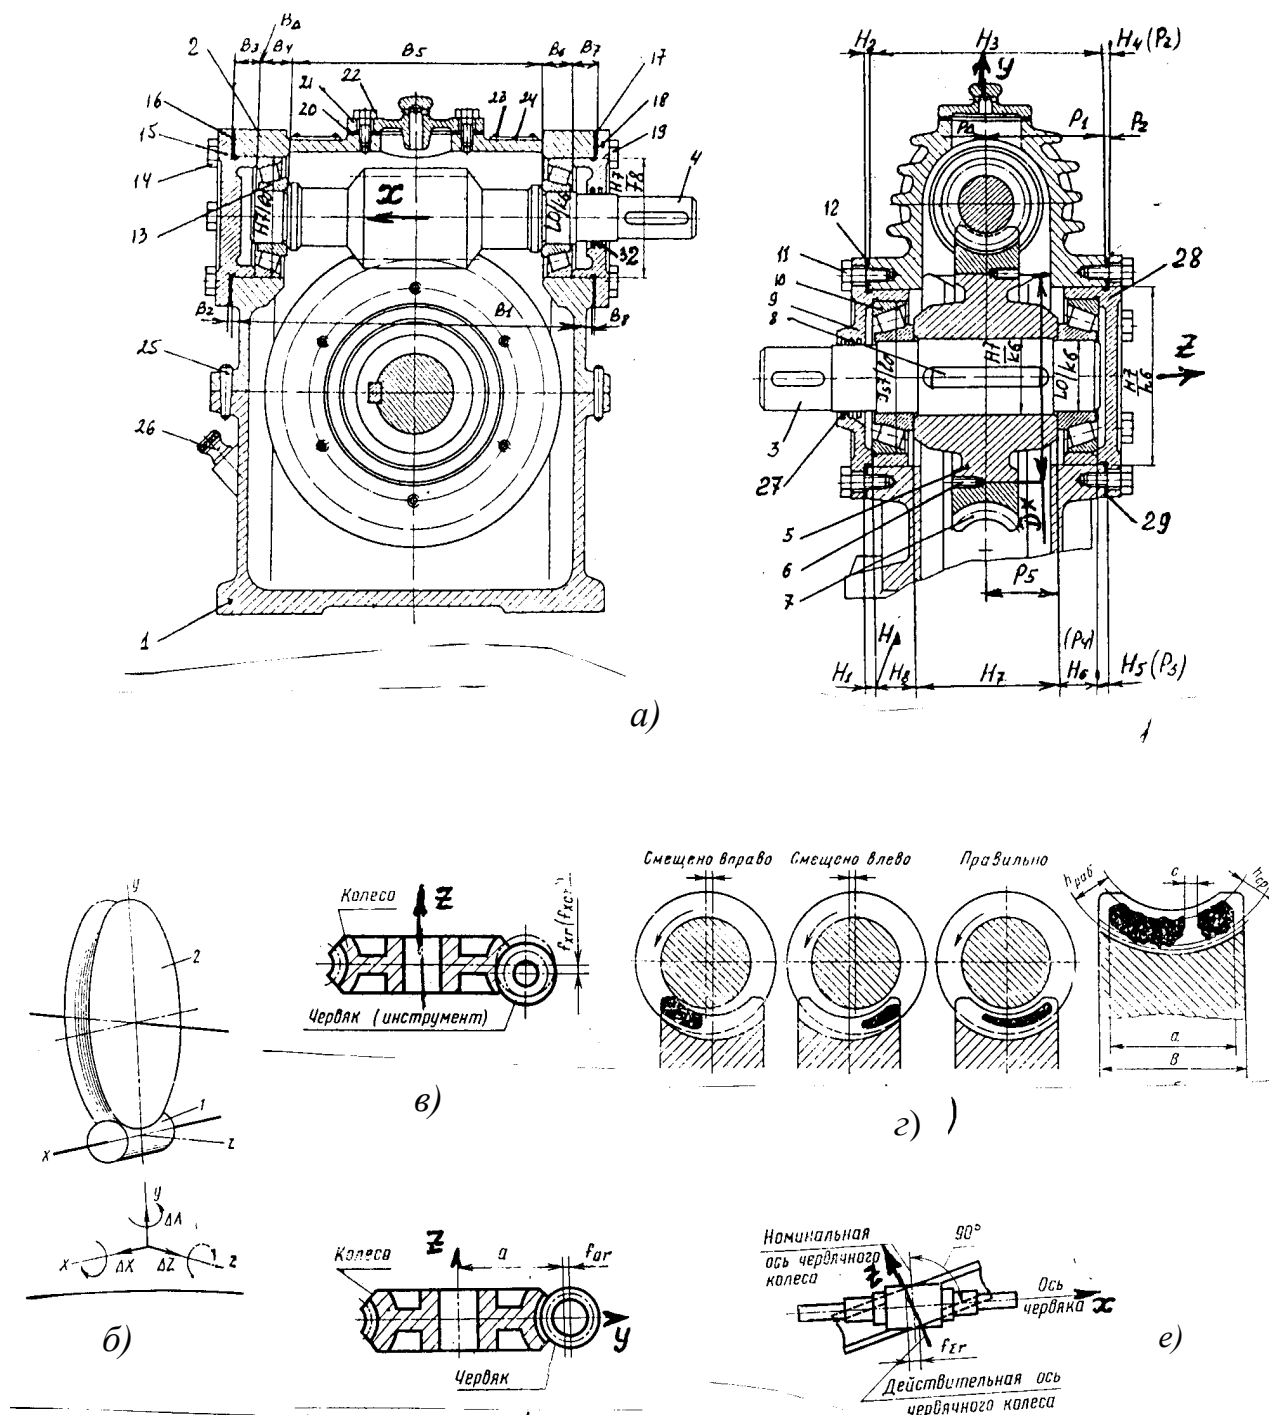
Исходные данные к сборке червячного редуктора
